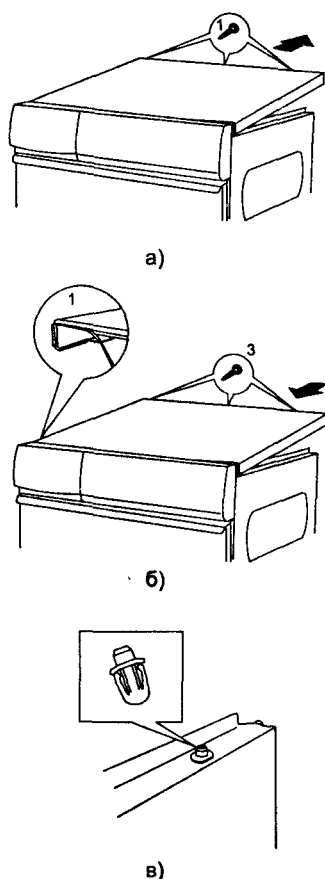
Операции с верхней крышкой: а — демонтаж крышки; б — монтаж крышки; в — удаление направляющих
